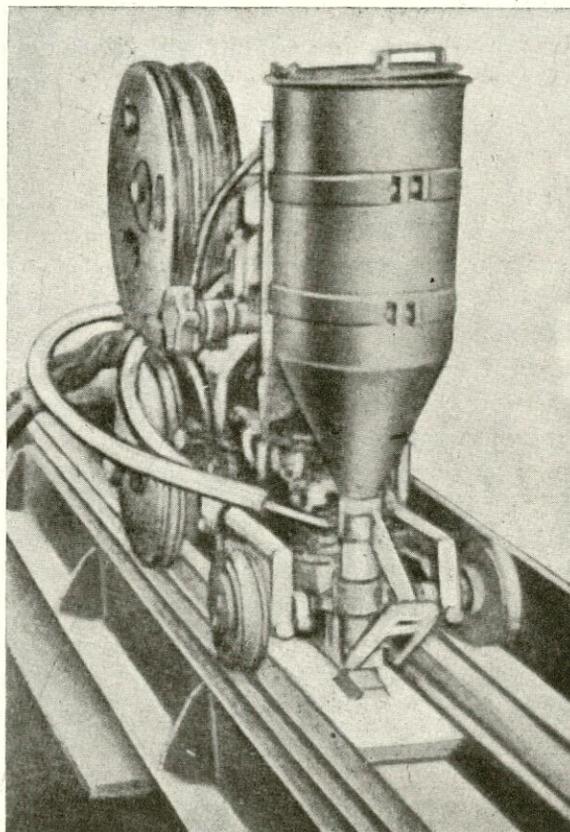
Equipo de soldadura TC-17-MA para la soldadura de planchas gruesas de aluminio.
